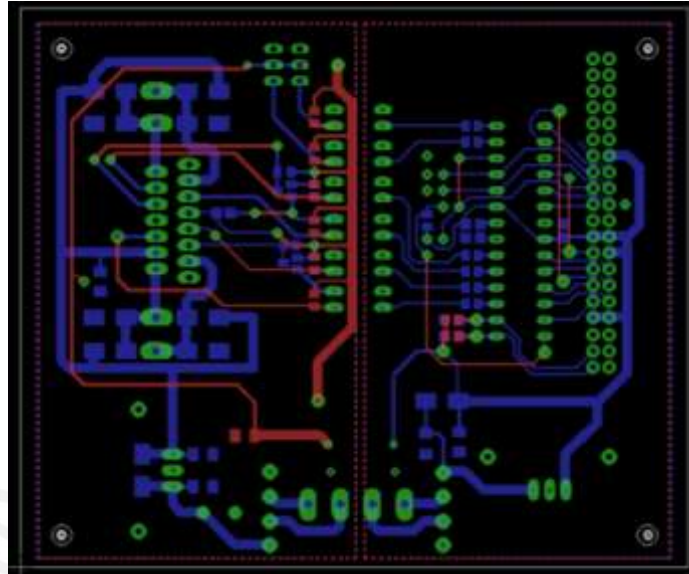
Cara de pistas: fuentes, controlador y motores.
